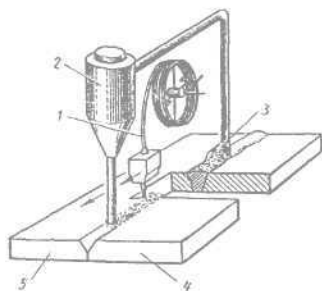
Автоматическая сварка под слоем флюса:
